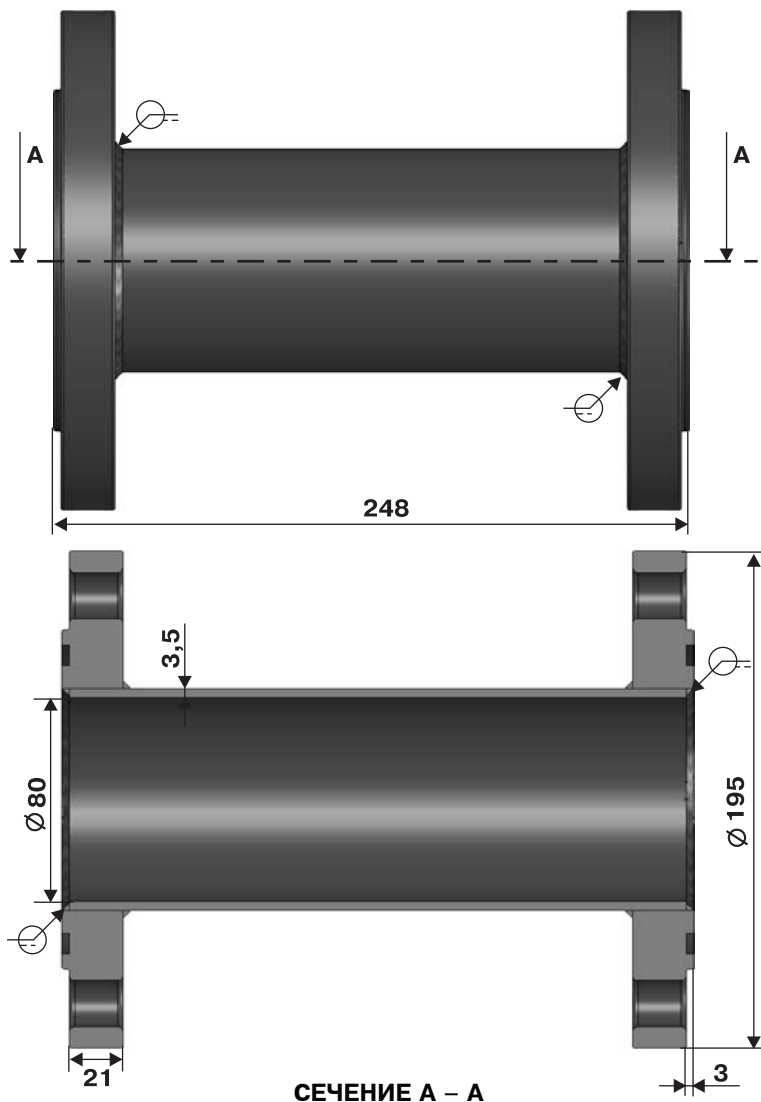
Габаритные и установочные размеры монтажной проставки ДУ80
